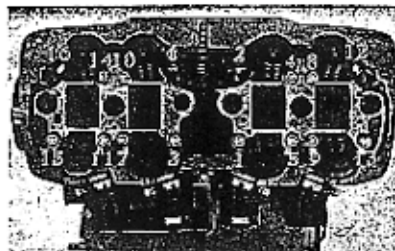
Ordine di serraggio dei dadi della testa.
